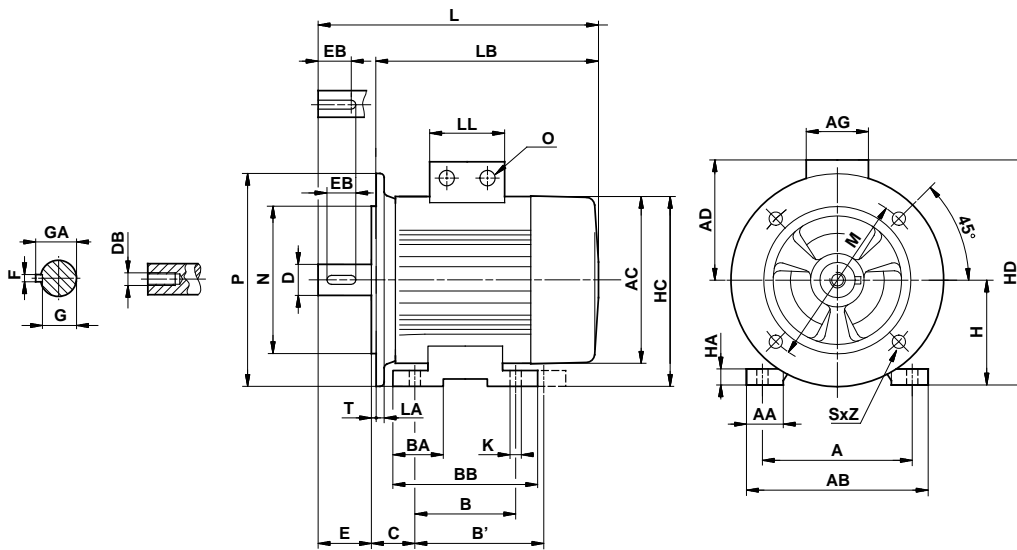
Foot-mounted motor with free-hole flange, IM B 35
